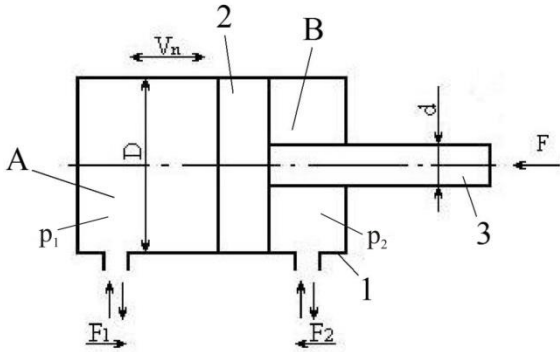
Гідроциліндр з однобічним штоком: 1 – циліндр (корпус); 2 – поршень; 3 – шток; А – поршнева порожнина; В – штокова порожнина
